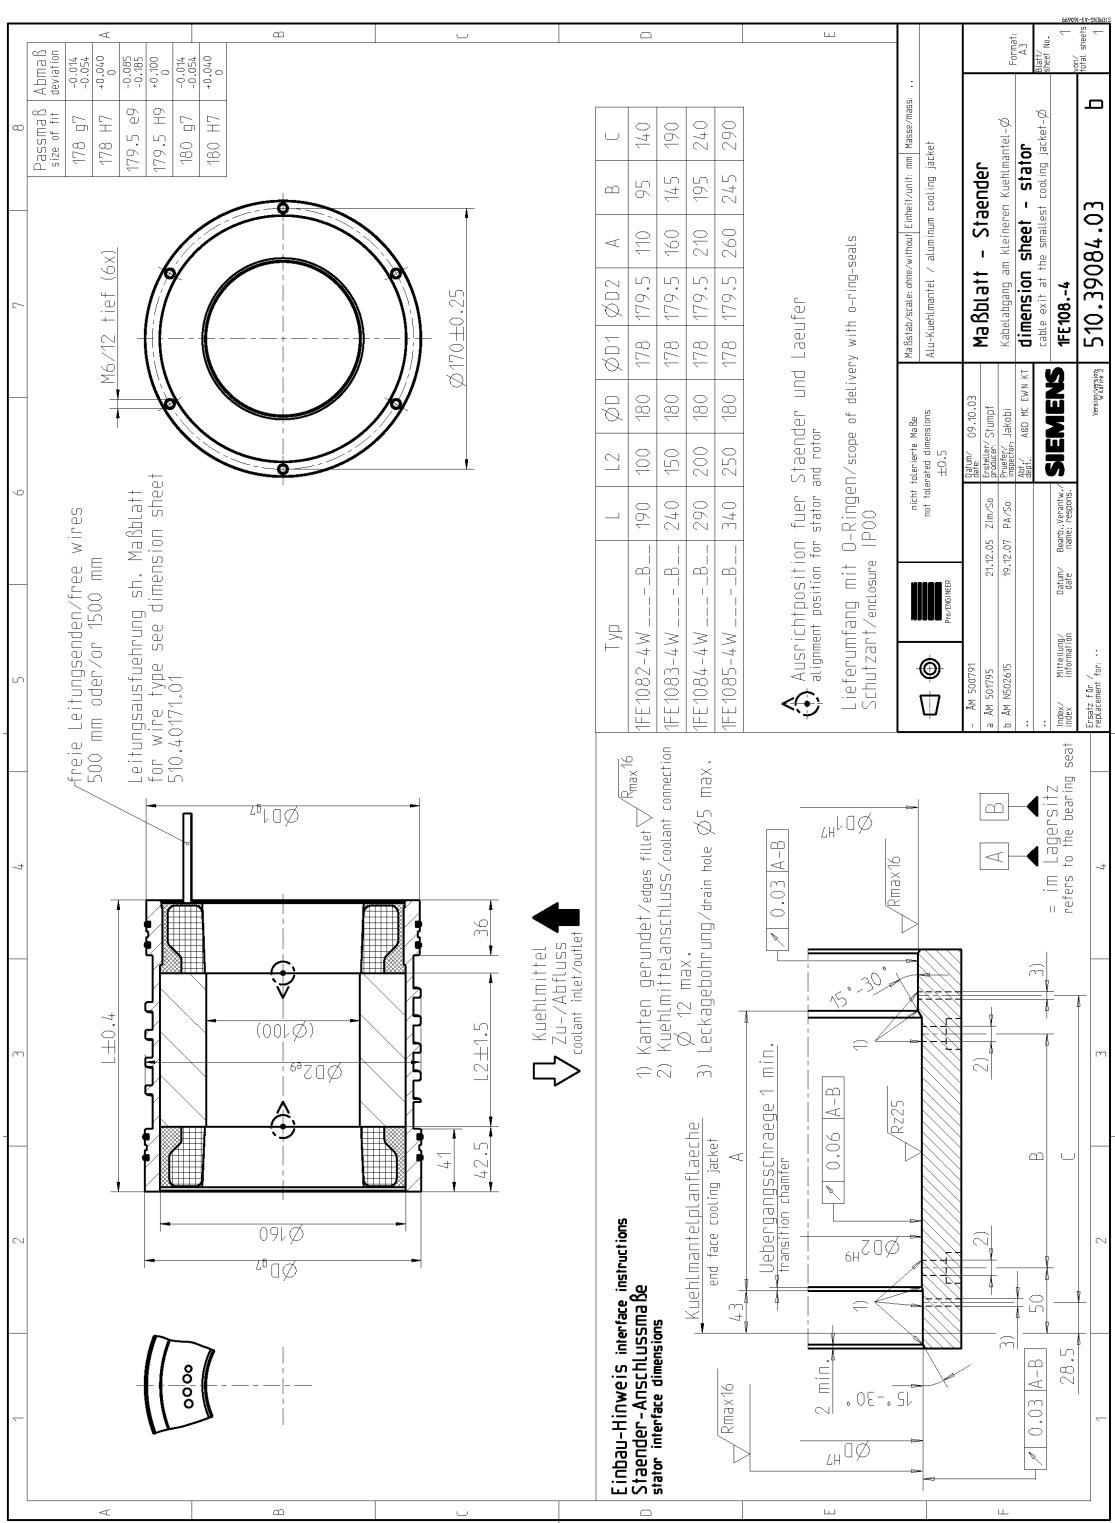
1FE108□-4, Ständer mit Kühlmantel, Kabelabgang am kleineren Kühlmanteldurchmesser
